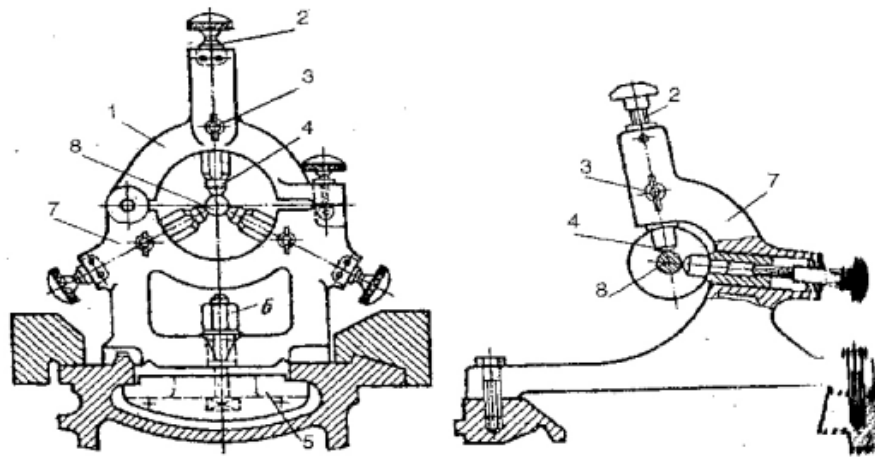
Конструкции люнетов: а – неподвижного; б – подвижного;
